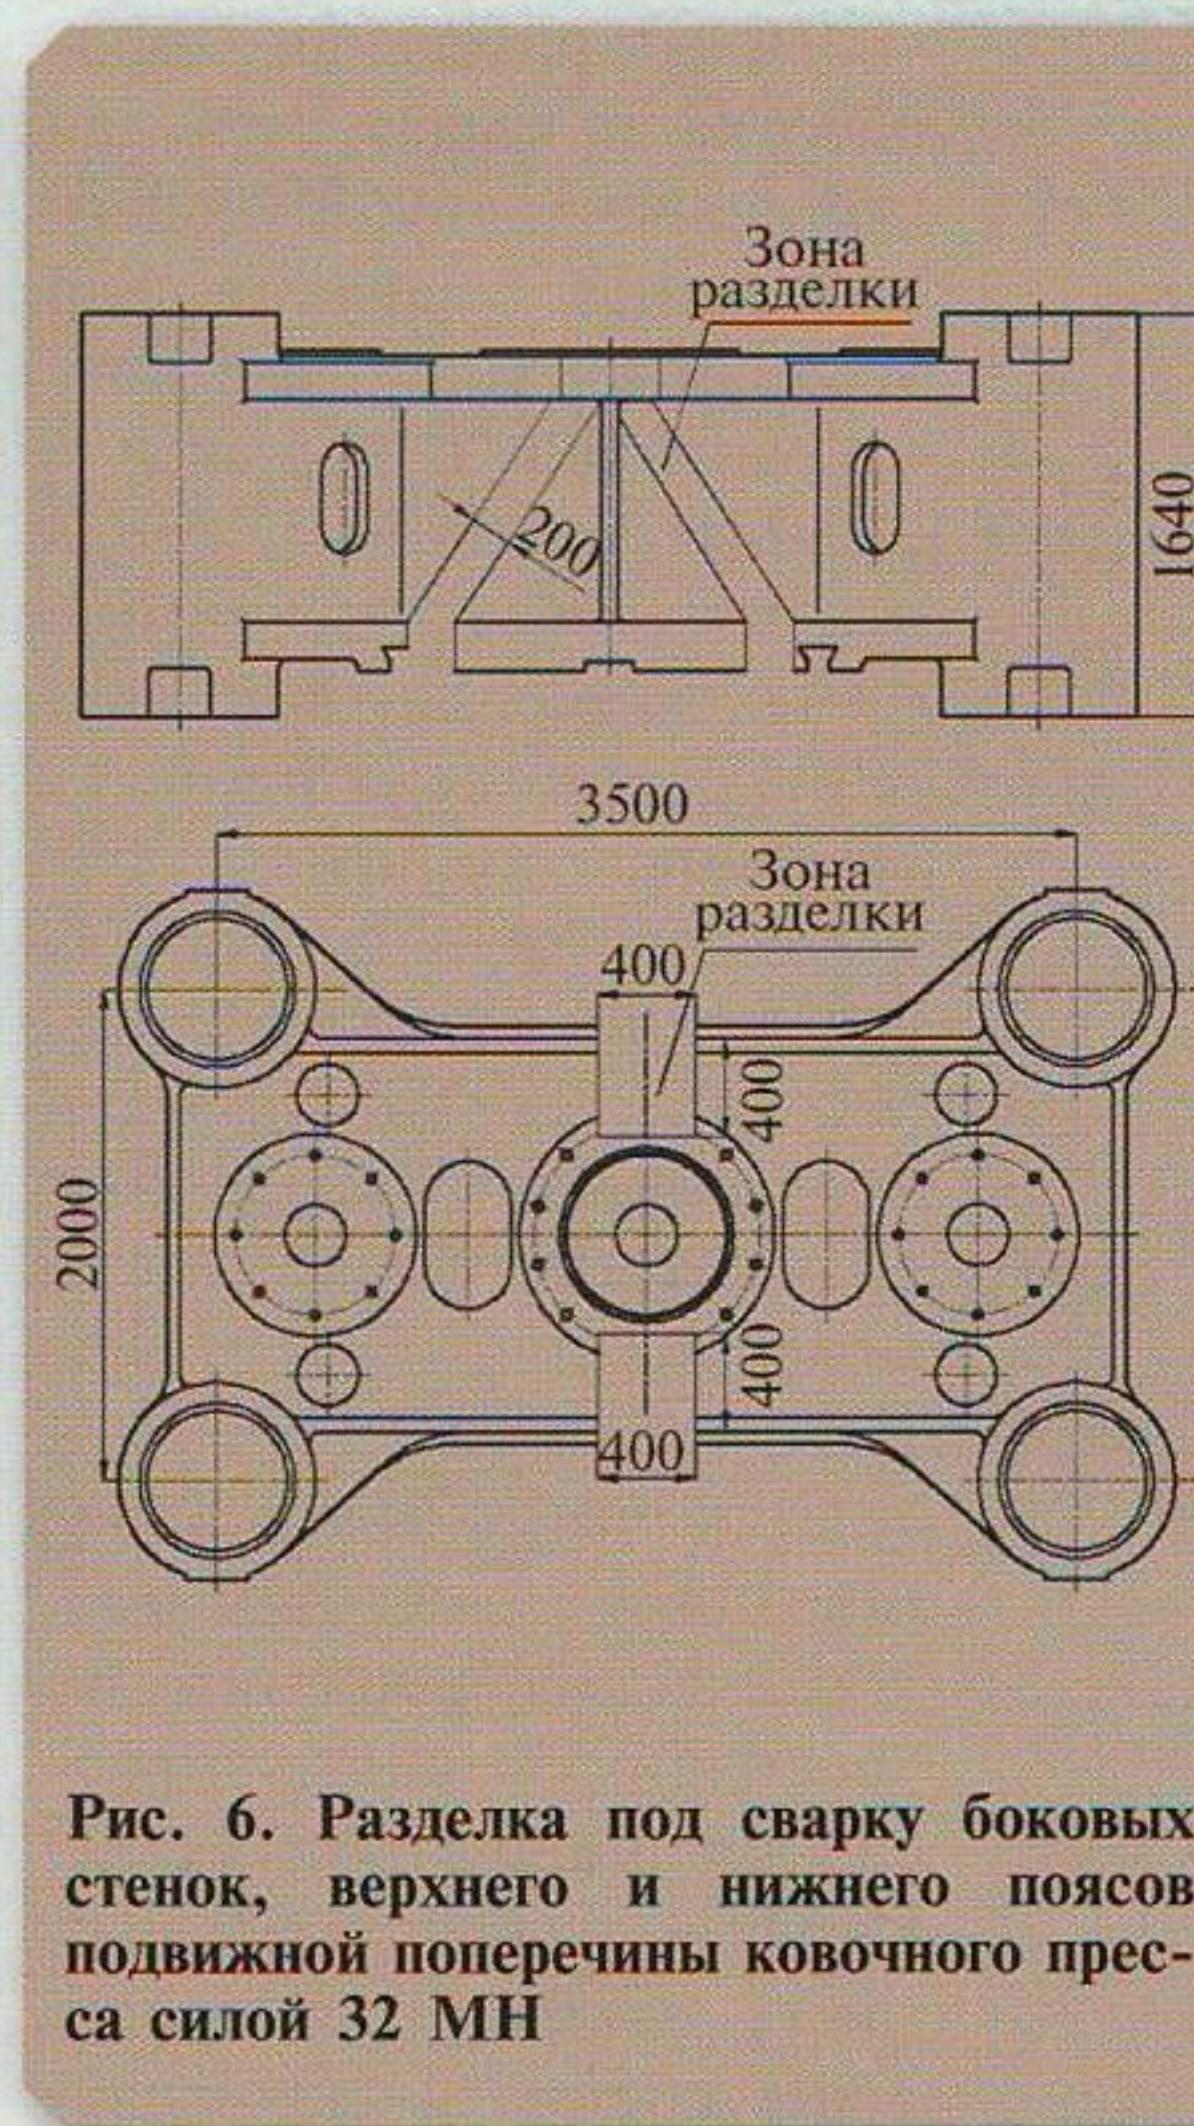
Разделка под сварку боковых стенок, верхнего и нижнего поясов подвижной поперечины ковочного пресса силой 32 МН
